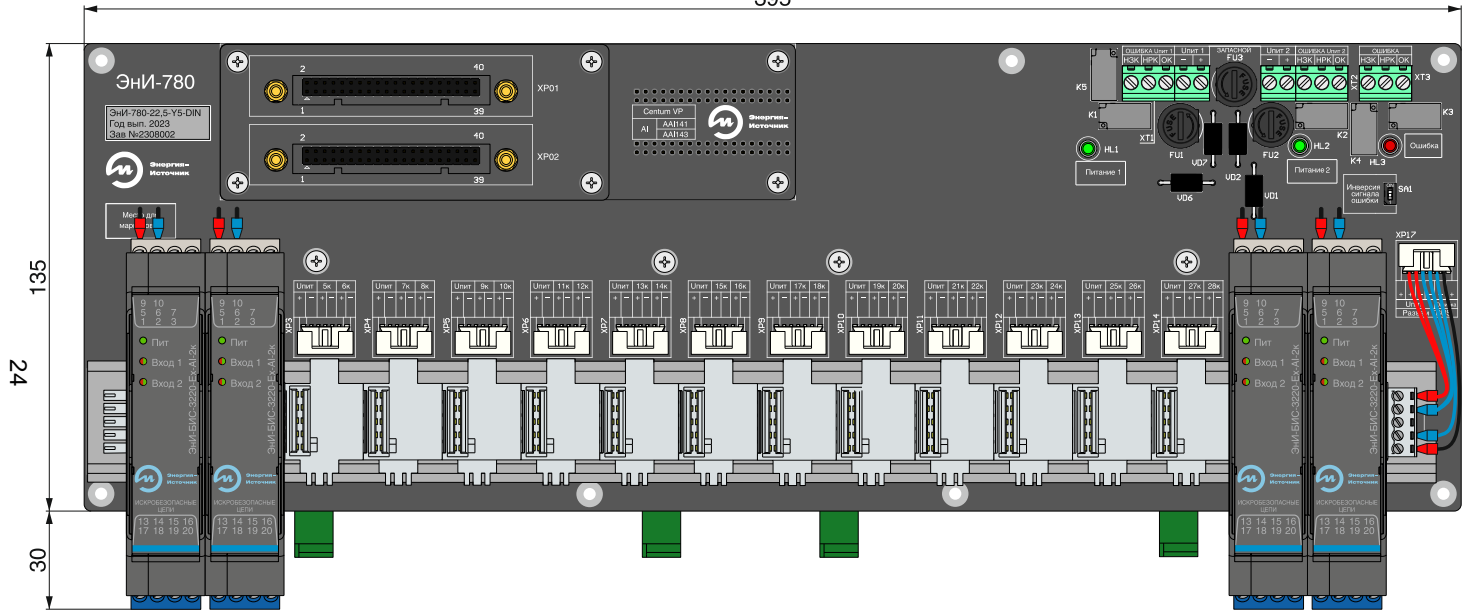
Габаритные размеры платы для шестнадцати приборов с корпусом шириной 22,5 мм
